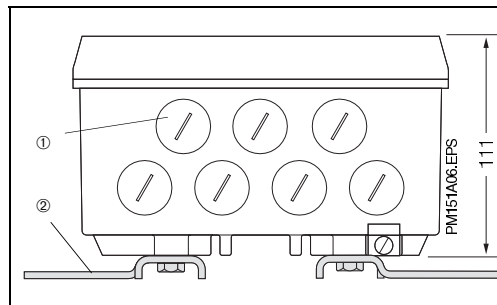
Fond du boîtier de protection avec plaques de fixation en place pour montage mural
